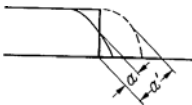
(Schlechtes) Abschmelzen von Blechkanten.
